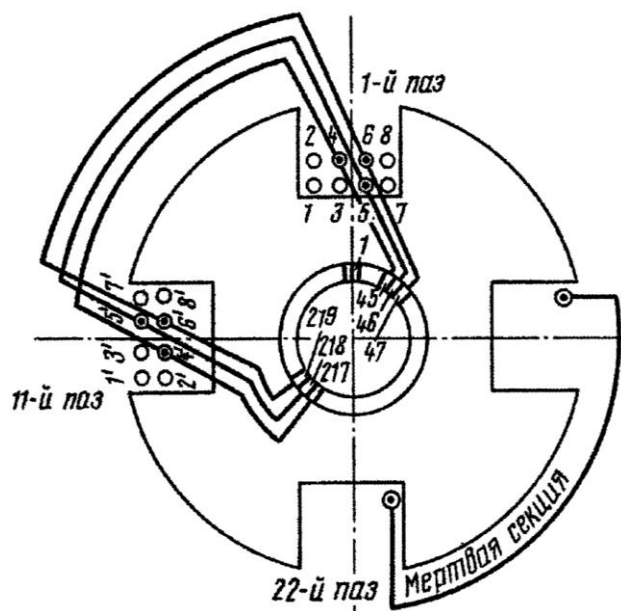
Схема соединения обмотки якоря электродвигателя ТЛ-110М
